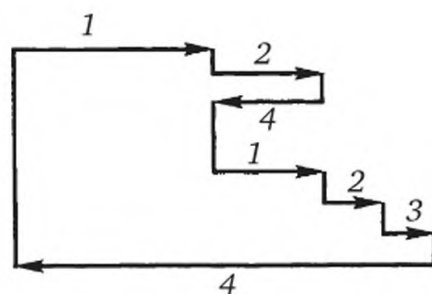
Схема варианта цикла глубокого сверления
